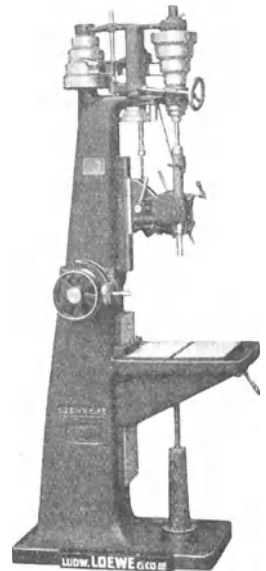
Schnellbohrmaschine mit Einscheibenantrieb, Bohrdurchmesser 2 bis 22 mm. (Löwe, Berlin.)
